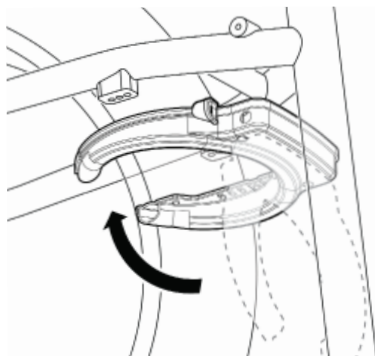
Instale el candado; posición de montaje del marco n.º 1
